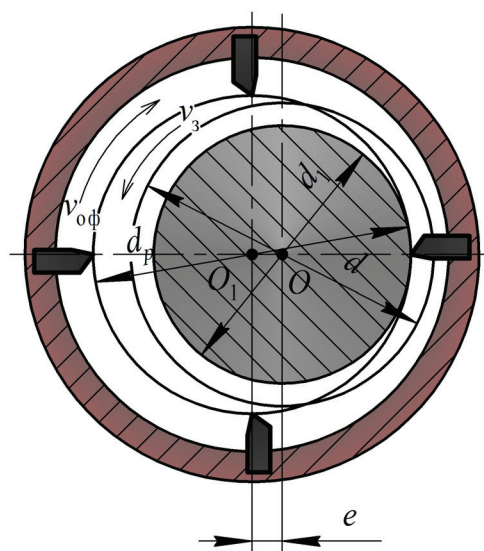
Схема нарезания резьбы охватывающей фрезой:
